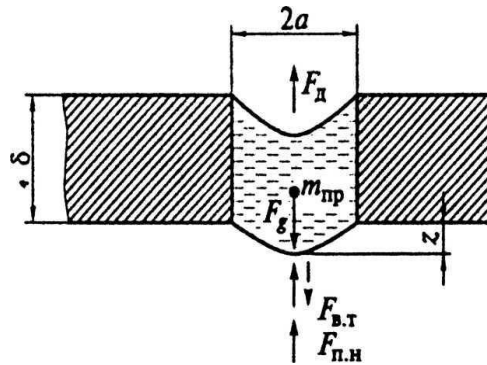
Сферическая модель сварочной ванны: F_d – сила давления дуги; F_g – сила тяжести сварочной ванны; $F_{в.т}$ – силы вязкого трения при колебании ванны; $F_{п.н}$ – силы поверхностного натяжения с наружной и внутренней поверхности сварочной ванны; a – полуширина сварочной ванны; m_{np} – приведенная масса сварочной ванны; δ – толщина свариваемого металла; z – провисание сварочной ванны [Spherical welding pool model: F_d – arc pressure force; F_g – gravity of the welding pool; $F_{в.т}$ – viscous friction force when the bath oscillates; $F_{п.н}$ – surface tension forces from the outer and inner surfaces of the welding pool; a – half-width of the primary bath; m_{np} – reduced mass of the welding pool; δ – thickness of the metal being welded; z – sagging welding pool]
